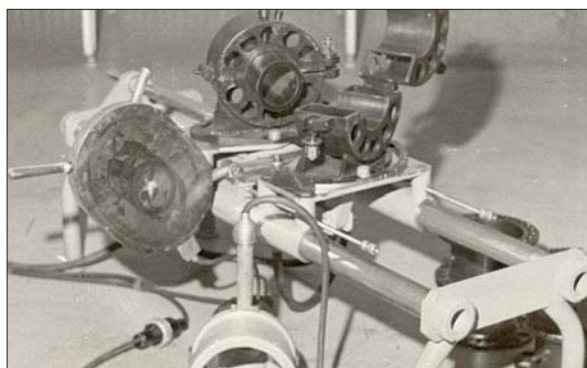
Станок с пневматическим приводом для сварки труб и фасонных деталей в конический раструб
